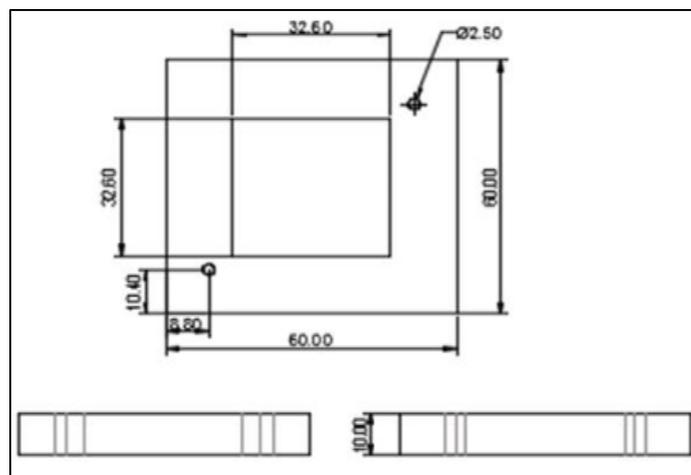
Desenho em CAD do suporte do dissipador.
